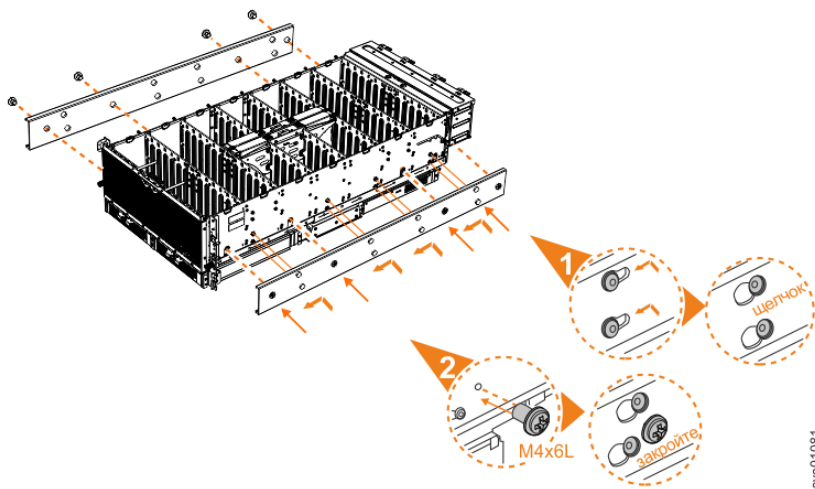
Прикрепление внутренней части направляющей к корпусу
